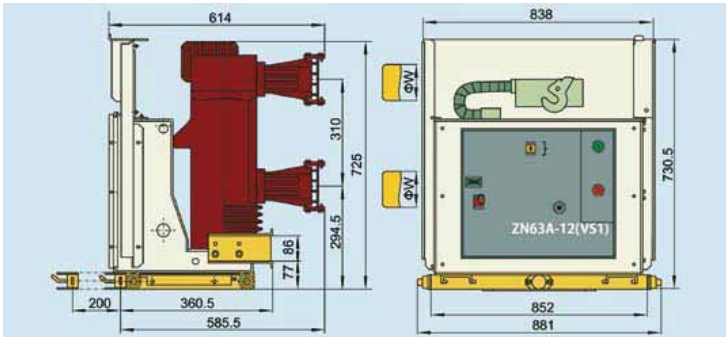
Внешний вид и монтажные размеры выключателей: ZN63A-12/T 4000-40, ZN63A-12/T5000-50
